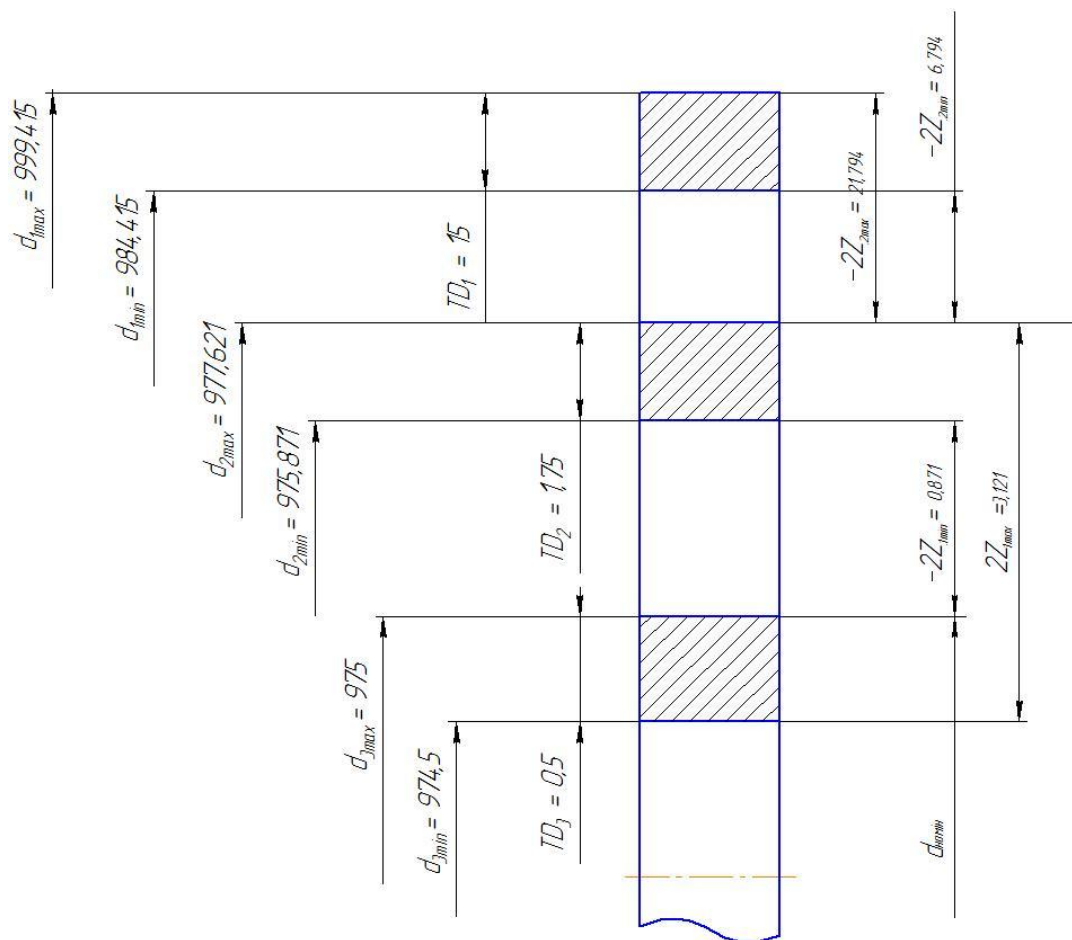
Схема графічного розташування припусків та допусків на обробку поверхні діаметром 975 мм, H12
